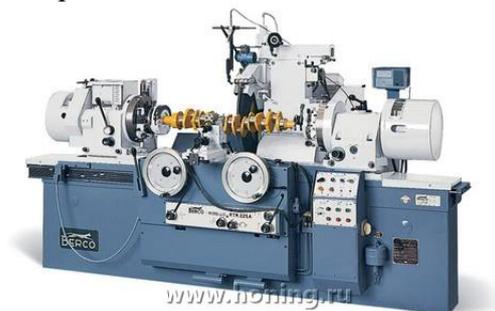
Шлифовальный станок для обработки коленчатых валов RTM 225A
